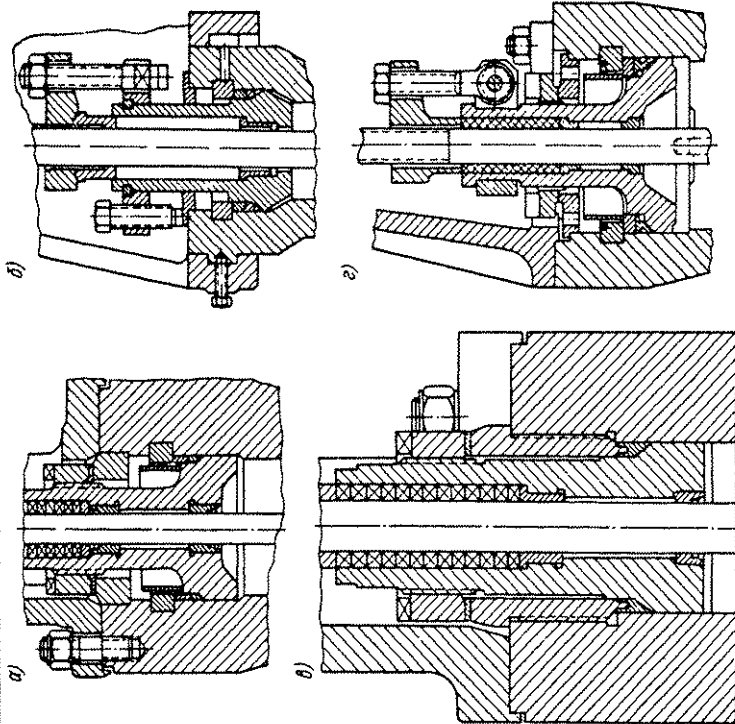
Конструкция бесфланцевых соединений крышки с корпусом: а и б — вентиль и задвижка  $D_y = 70$  мм,  $P_{\text{раб}} = 300$  кг/см<sup>2</sup>,  $t = 650^\circ\text{C}$ ; в — конструкция с резьбовым упором; г — конструкция с упорным кольцом
